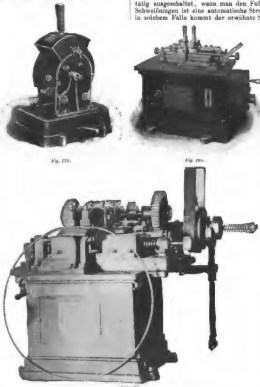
2. A. Elektro- und Schweißapparat Typen 80 A, 2 A, 2 A A.
